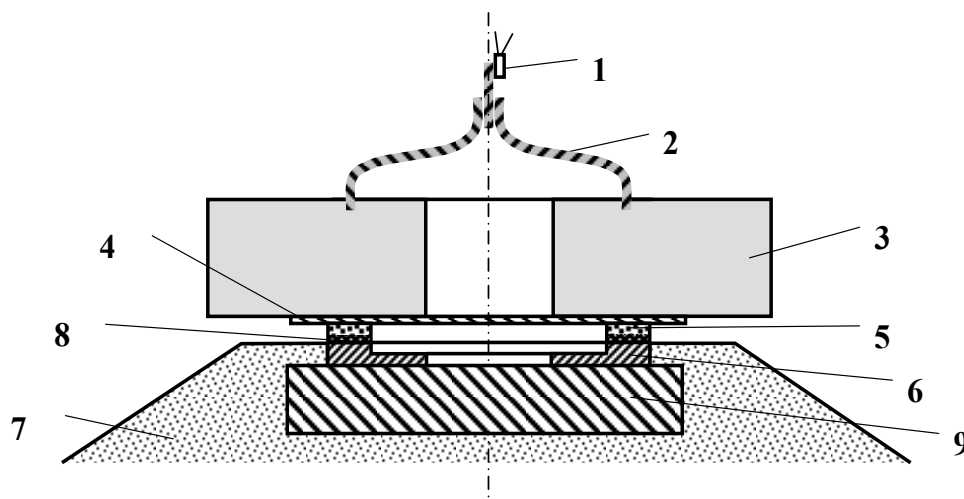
Схема нанесения покрытий на поверхность трения заготовки кольца разгрузки:
